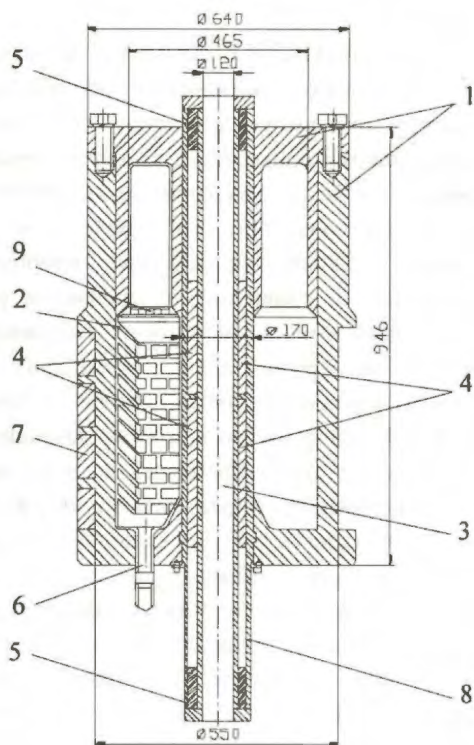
Корпус АЗ реактора ЯГУАР: 1 – внешняя силовая оболочка корпуса с крышкой; 2 – ампула; 3 – центральный экспериментальный канал; 4 – ИС (сведены к центру АЗ); 5 – амортизаторы механизма ИС; 6 – сливной трубопровод; 7 – свинцовая биологическая защита (неподвижная часть); 8 – внутренняя силовая оболочка (гильза); 9 – фланец жесткости; 10 – свинцовая биологическая защита (подвижная часть); 11 – опорная плита; 12 – подвеска корпуса. Размеры в миллиметрах
